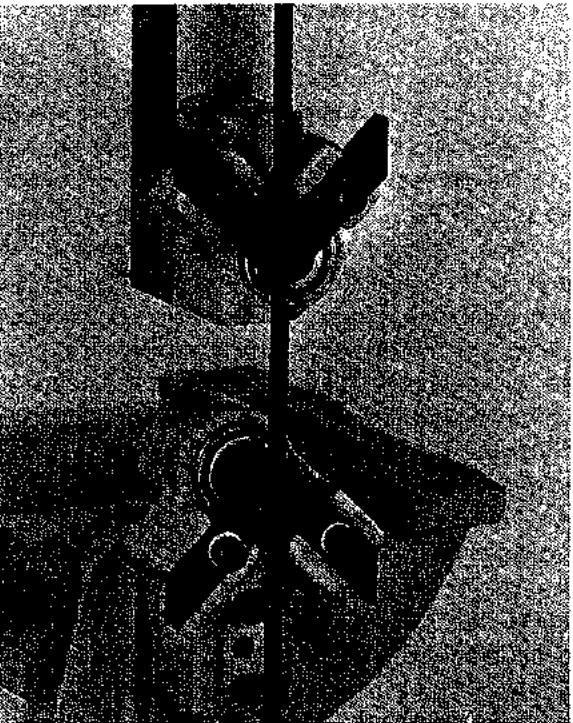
Guías de sierras de cinta, del tipo insertado (DoAll Co.)
